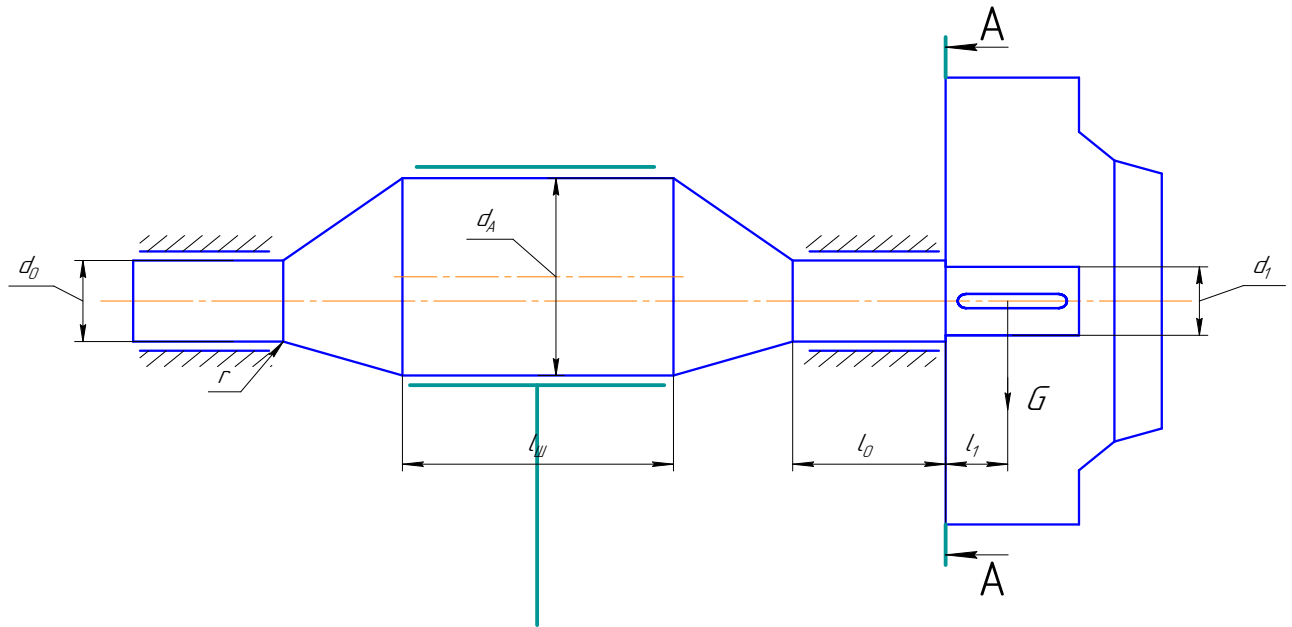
Розрахункова схема одношатуного ексцентрикового вала
